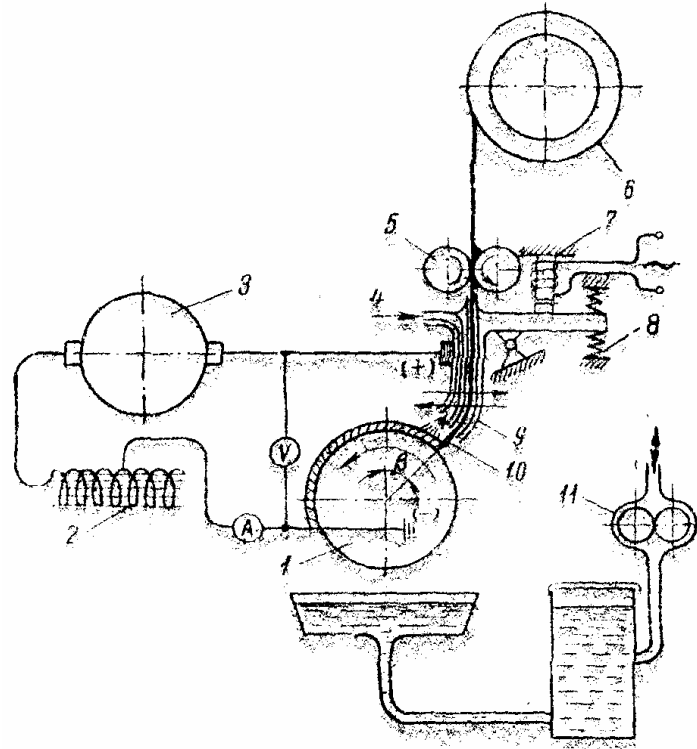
Схема автоматичної електроімпульсної установки для наплавлення деталей
